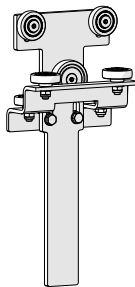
084293-4; Eindrückwerkzeug für Dichtlippen
